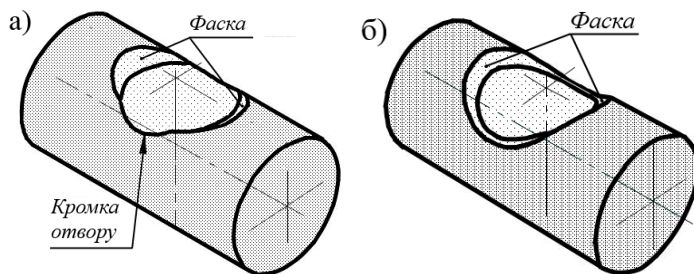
Виріб із ПКМ циліндричної форми з отвором: а) стан кромки отвору після обробки універсальним осьовим інструментом; б) рівномірно нарізана фаска
